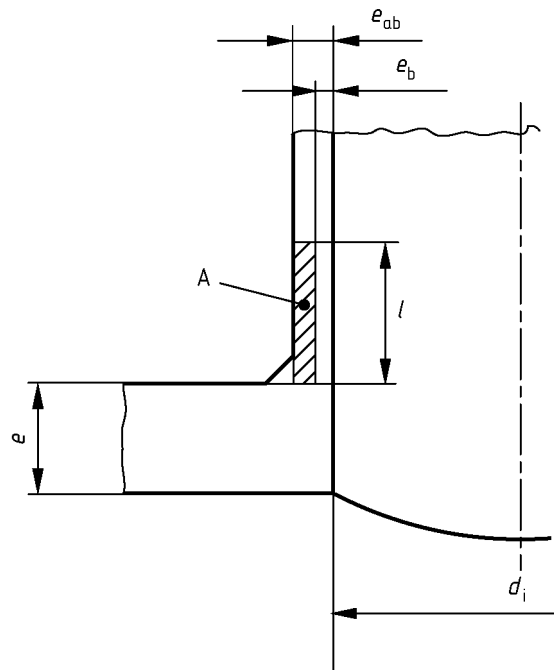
Manguito superpuesto en un fondo plano
